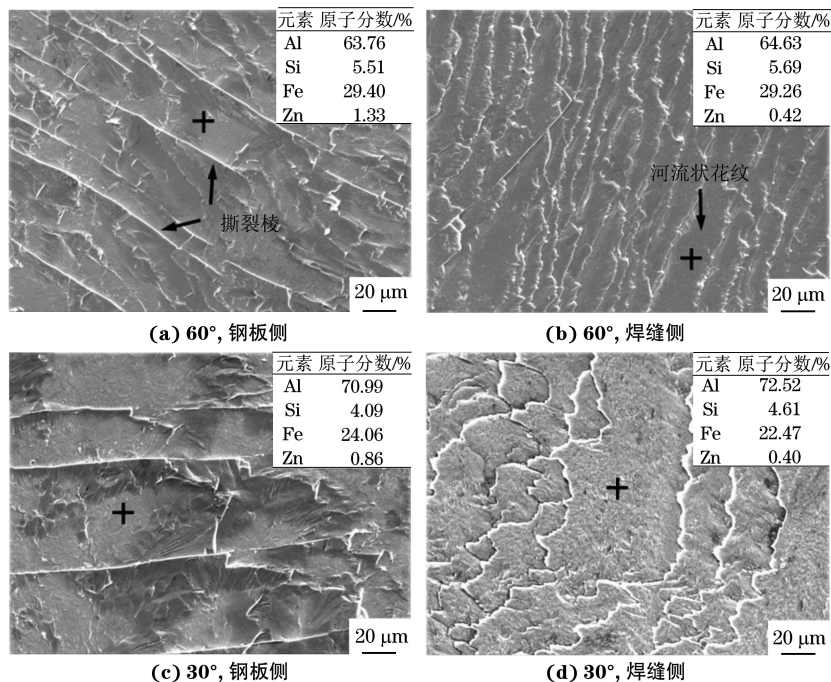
不同坡口面角度钢板/铝合金板焊接接头拉伸断口形貌
